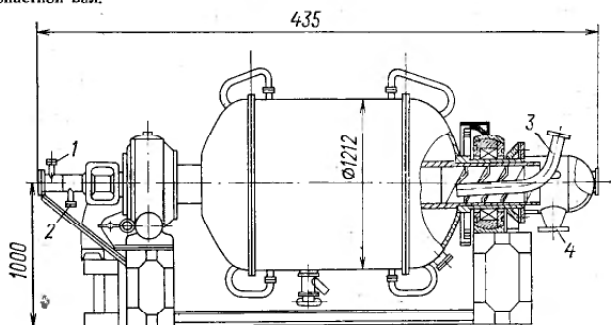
Барабанная вакуумная сушилка типа ВВС с вращающимся корпусом:
